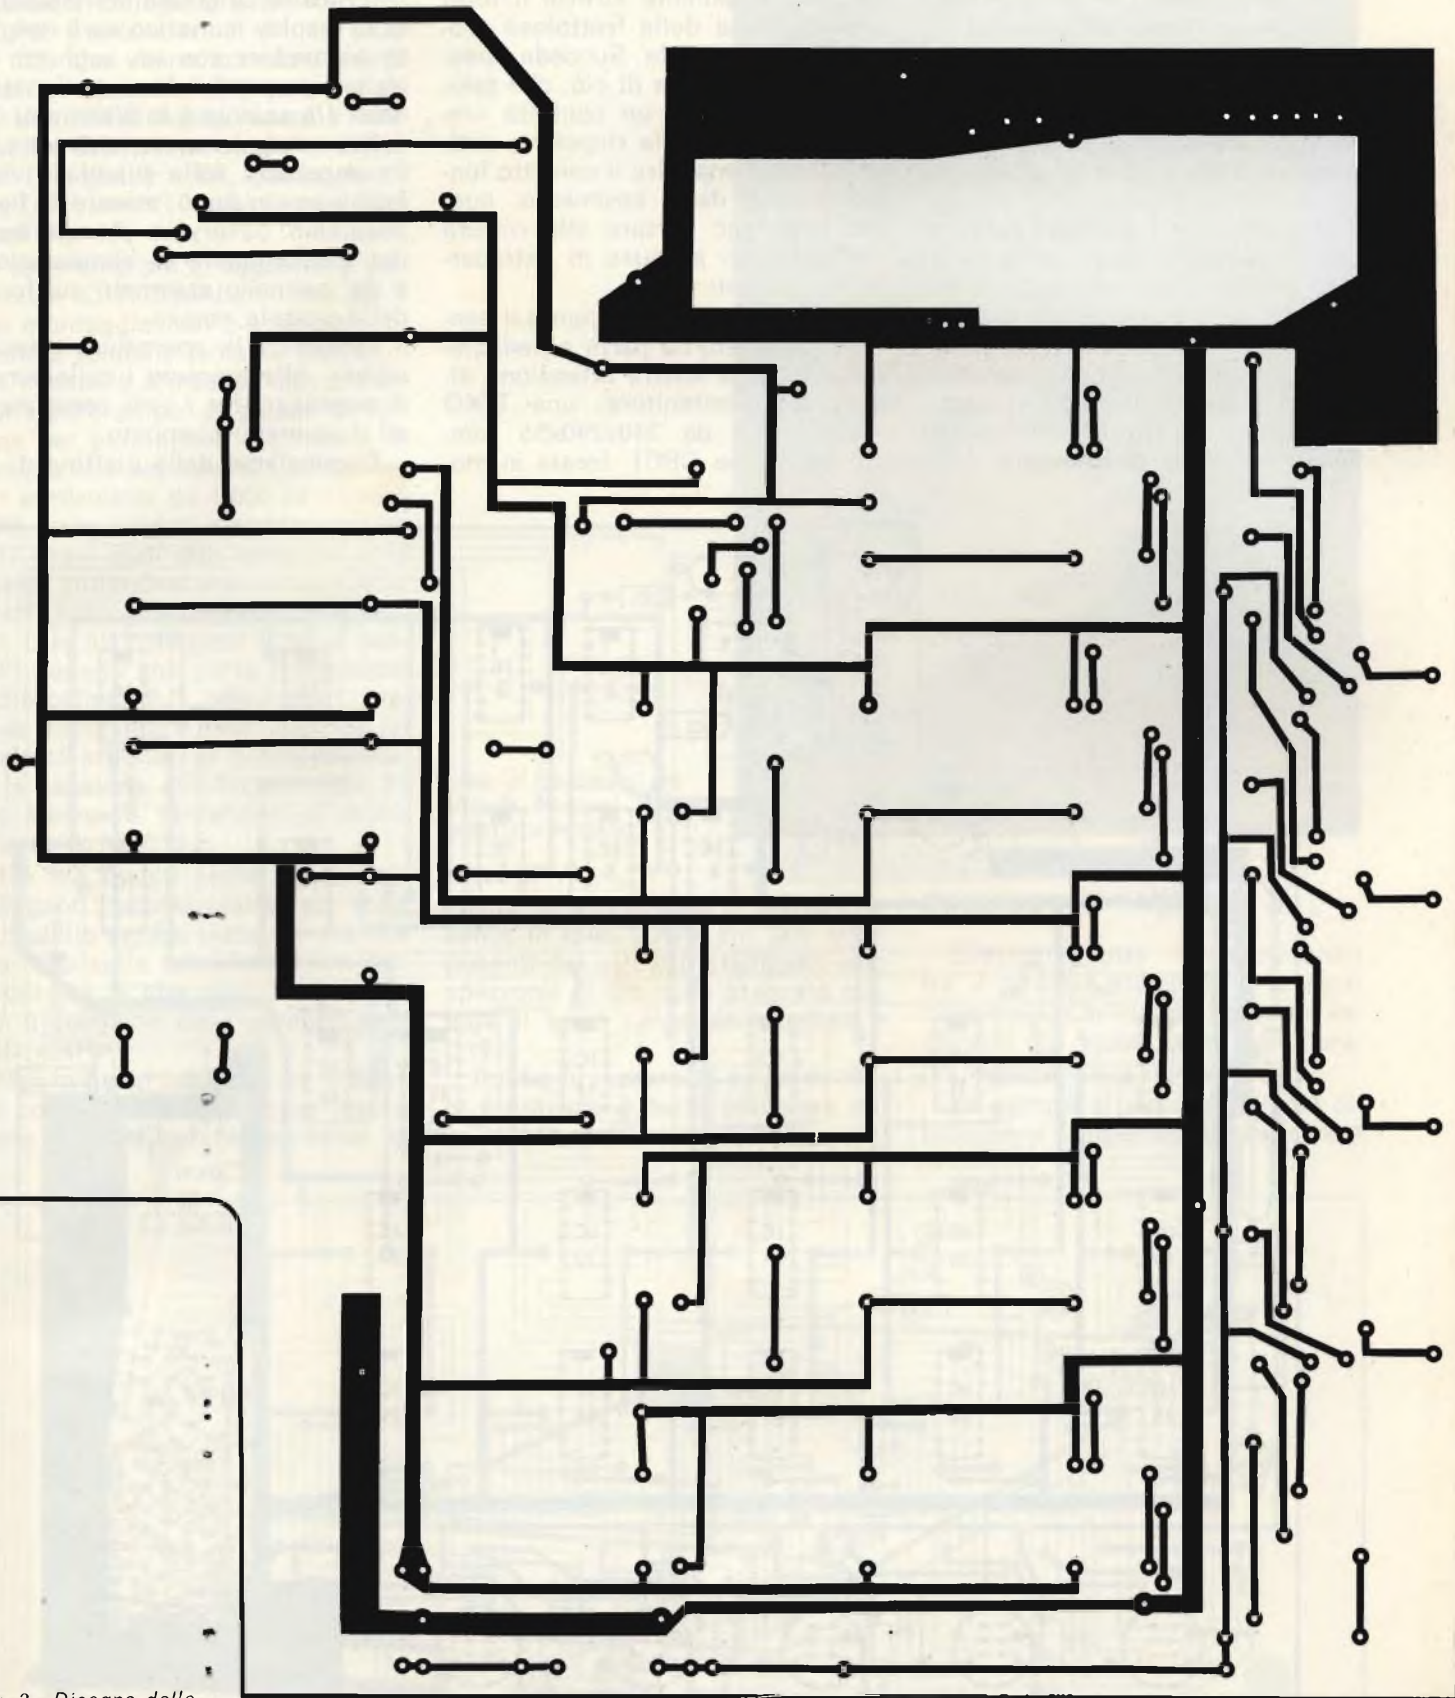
Disegno delle piste ramate sul lato componenti della ba-setta stampata.
